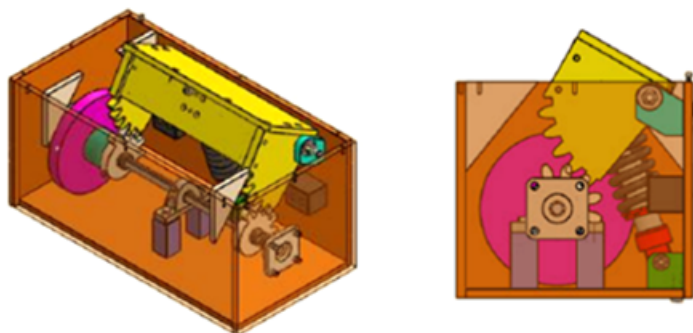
Преобразователь движения в виде зубчатого сектора и зубчатого колеса
